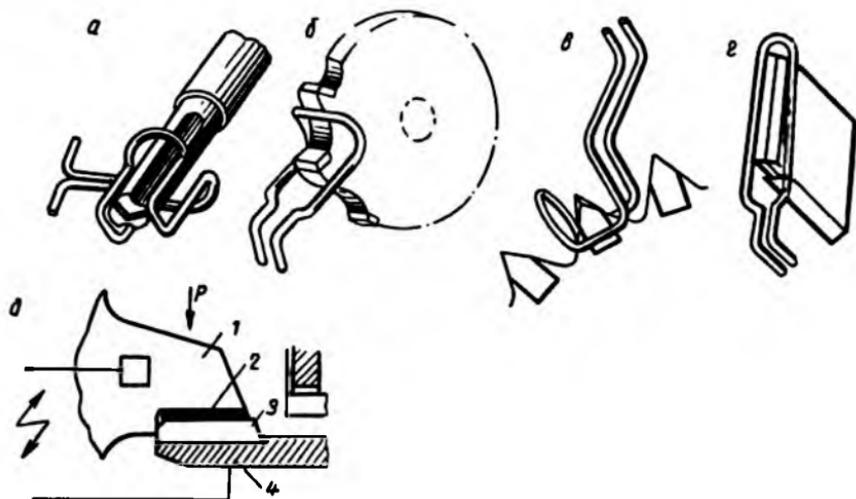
Индукторы для напайвания пластинок из твердого сплава на дереворежущий инструмент:
